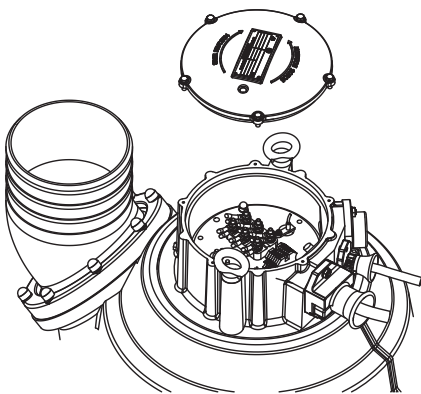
Montage du support de la plaque à bornes (J 604)
